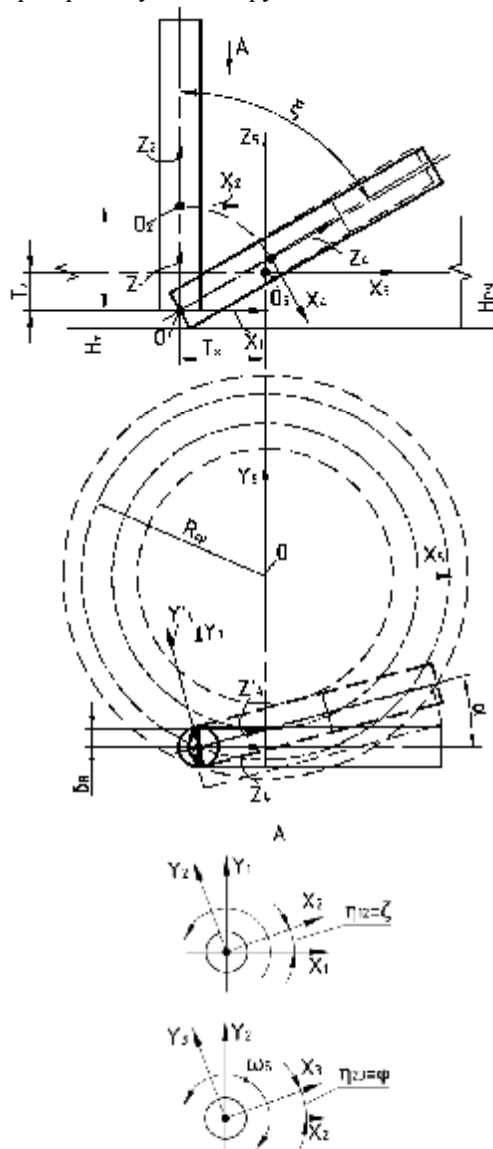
Схема установки свердла в робоче положення в роторному верстатi та система координат
